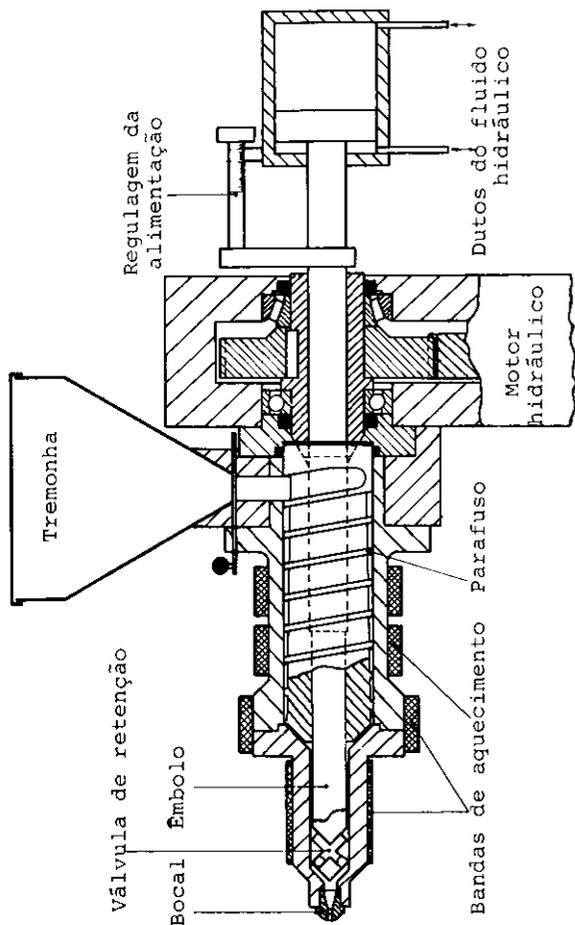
Injetora coaxial de parafuso e êmbolo.
